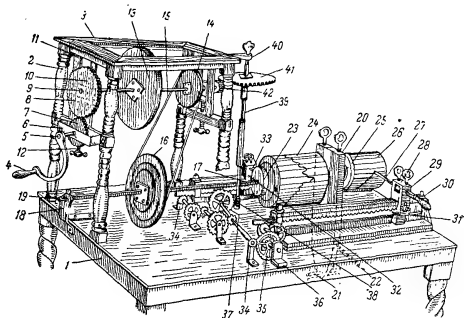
Кинематическая схема токарно-копировального станка. 1712 г. По А. С. Бриткину.
